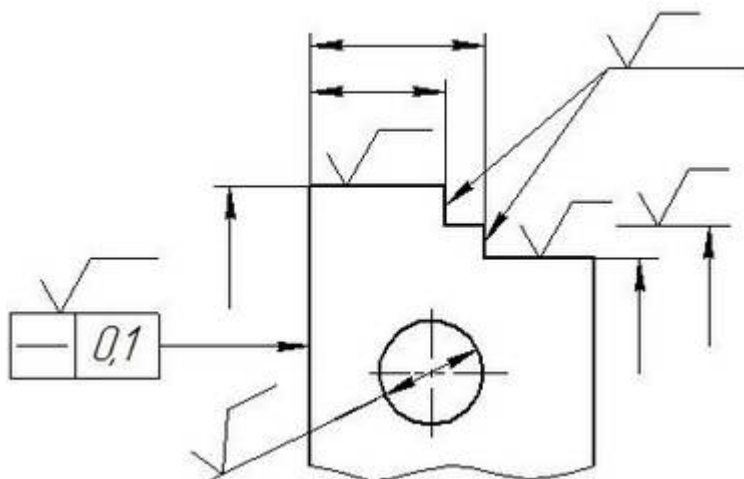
Схема обозначения шероховатости поверхностей на изображении изделия
